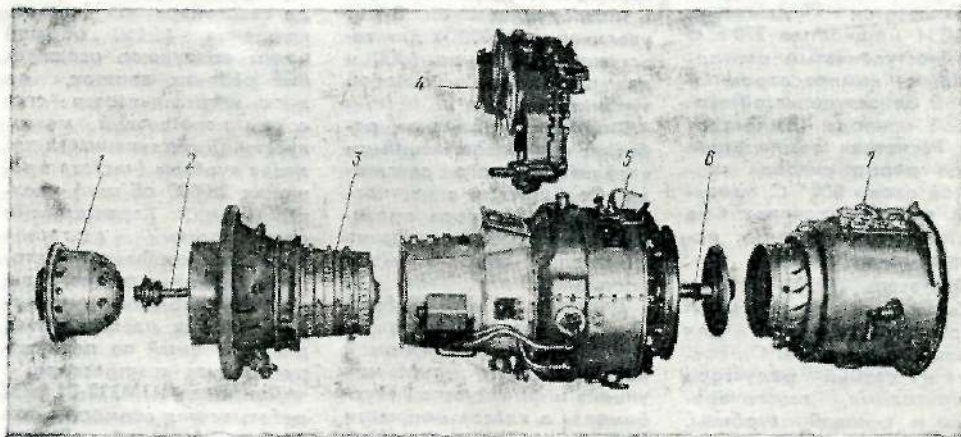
Модули двигателя GEM-2: 1 — редуктор; 2 — вал силовой турбины; 3 — корпус входного устройства и четырехступенчатый осевой компрессор; 4 — коробка приводов; 5 — каскад высокого давления с промежуточным корпусом компрессора и камерой сгорания; 6 — одноступенчатая турбина низкого давления; 7 — двухступенчатая силовая турбина
